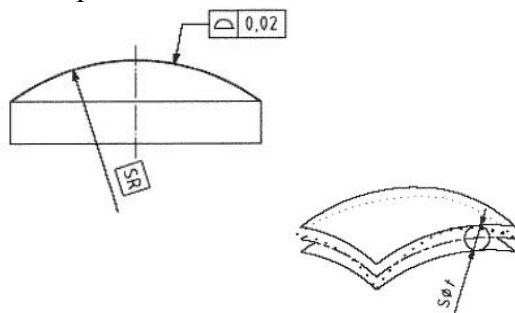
Označení a vysvětlení geometrické tolerance tvaru profilu čáry [4]
